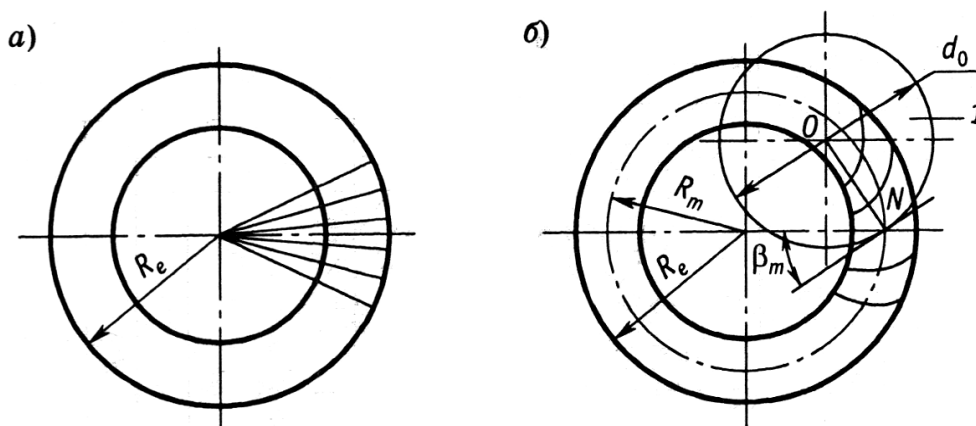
Формы зубьев конического колеса: a – прямые; b – круговые
